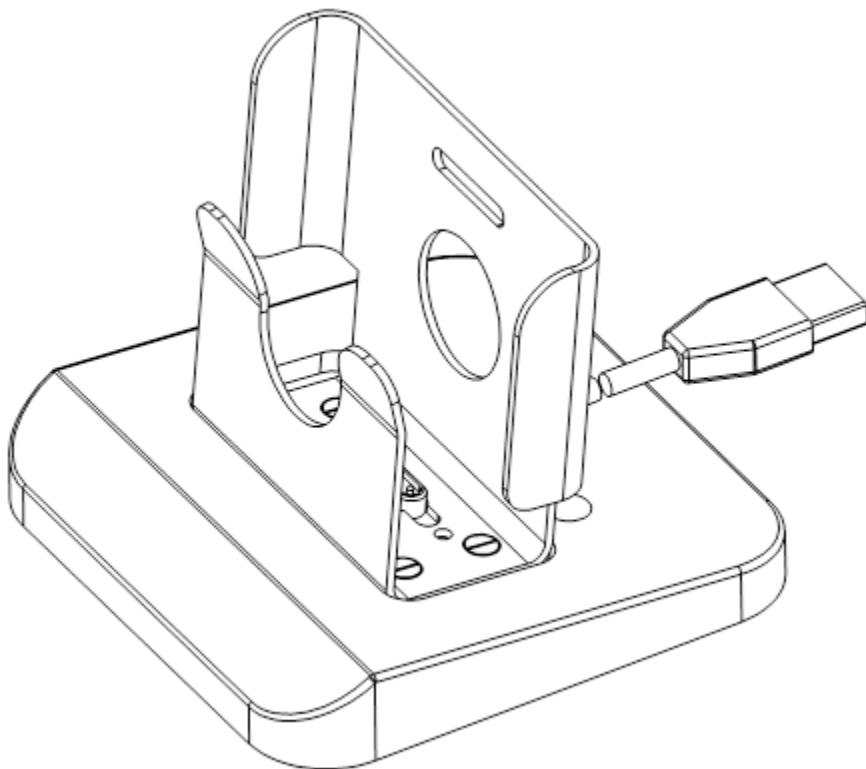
Эскиз общего вида считывателя ДАИ-5
